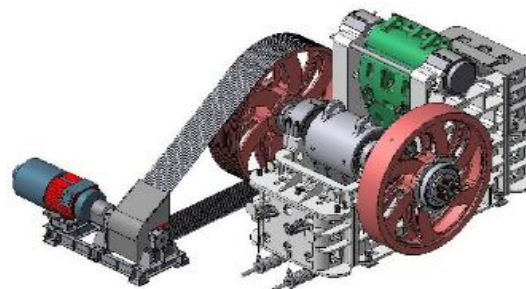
Общий вид щековой дробилки с простым движением подвижной щеки типа ЩДП
